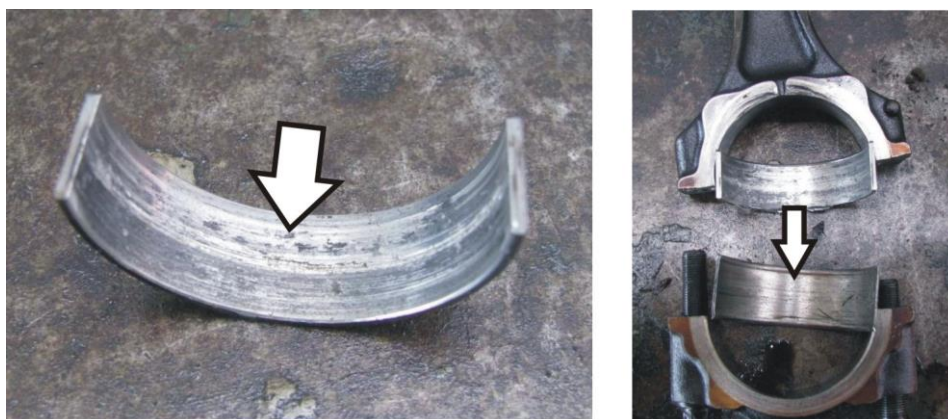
Изношенные детали двигателя легкового автомобиля. Следы схватывания на вкладыше – а. Полосы скольжения – б.
